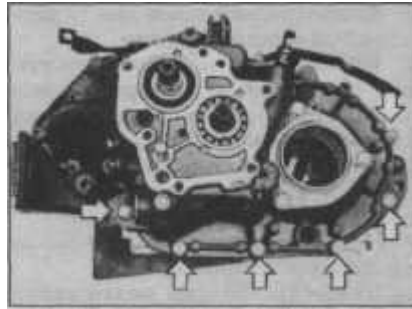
Шесть из болтов крепления картера коробки передач к ее задней крышке (отмечены стрелками) - внешняя сборка рычага выбора снята (Глава 7)
